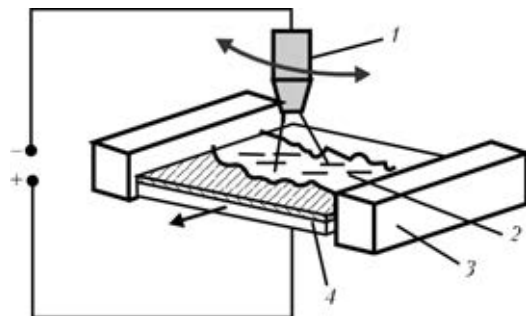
Схема работы плазменно-дуговой установки ОБ-1957: 1 — плазмотрон; 2 — ванна жидкого металла; 3 — кристаллизатор; 4 — обрабатываемая заготовка
